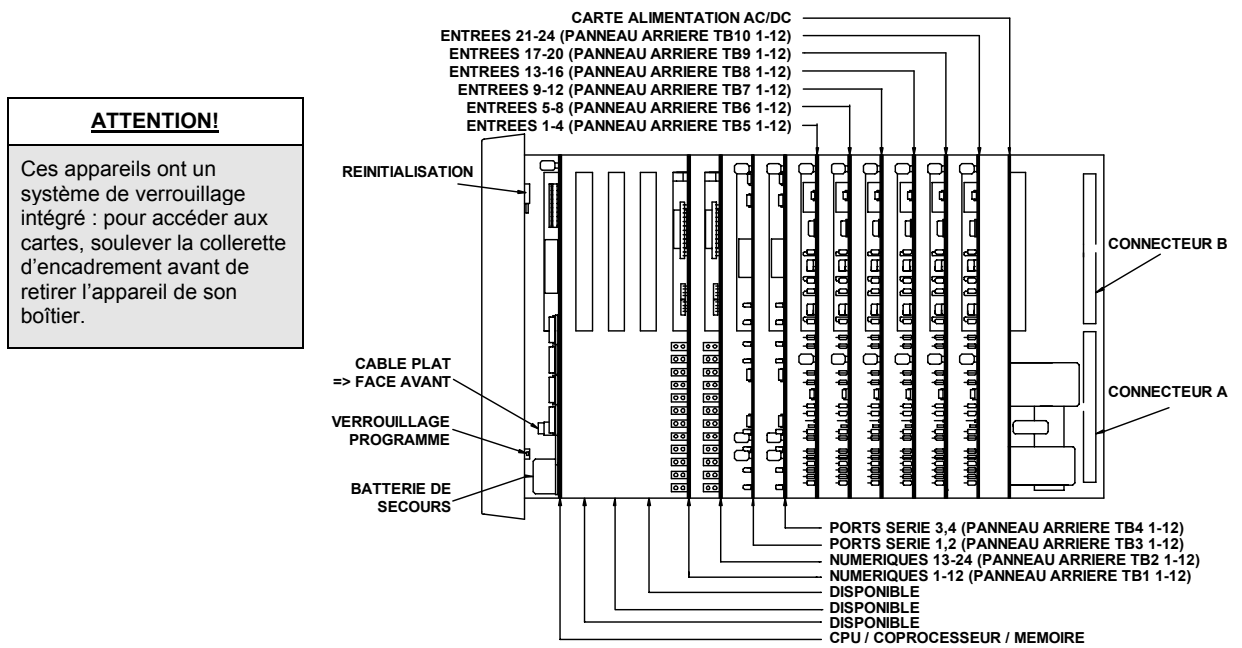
Carte Fond de Panier équipée de l'Omni 6000
